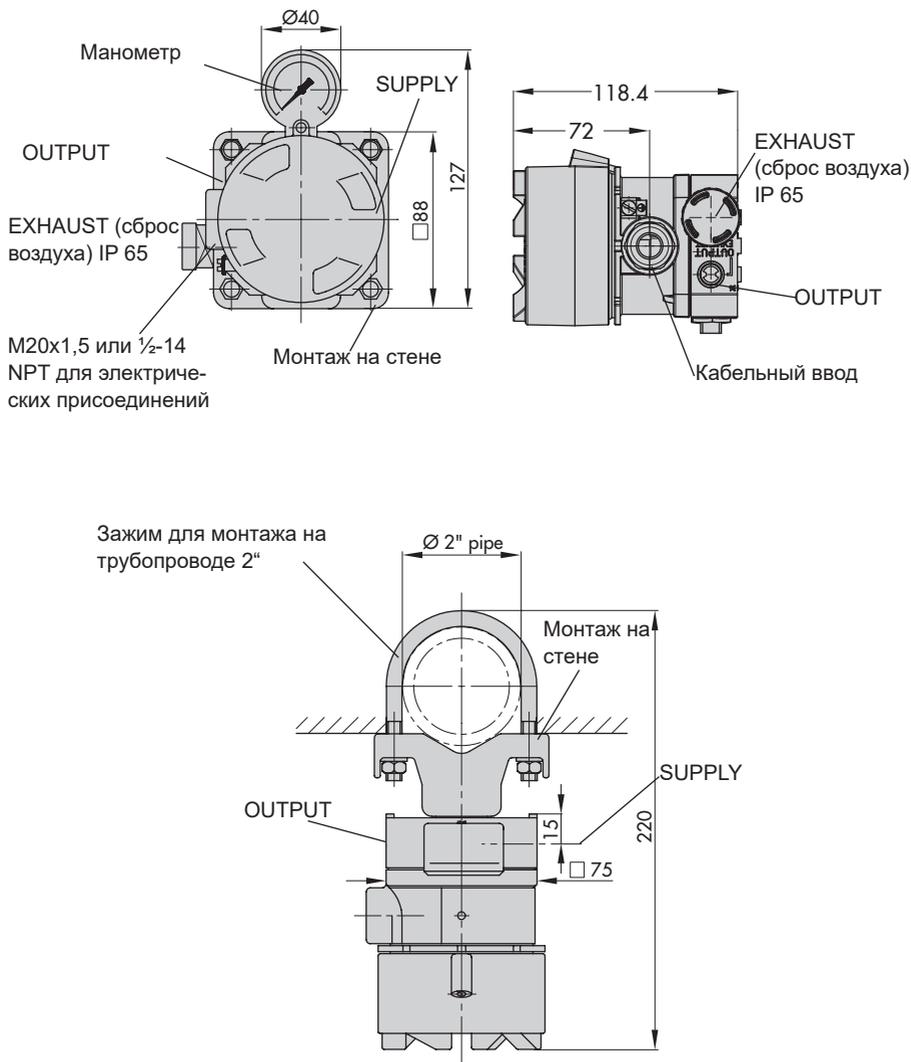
Габаритные чертежи для монтажа на стене и трубопроводе
